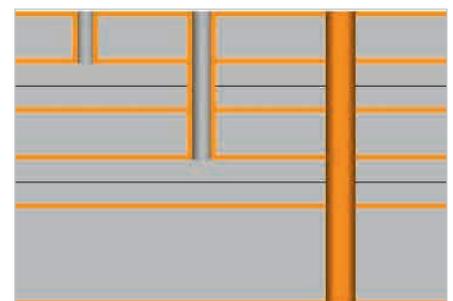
Шестислойная печатная плата с тремя видами отверстий
